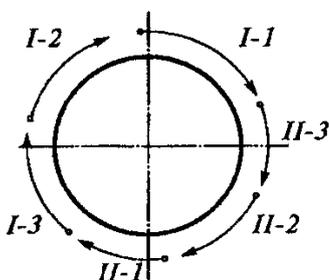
Порядок наложения корневого шва горизонтального стыка при сварке двумя сварщиками
